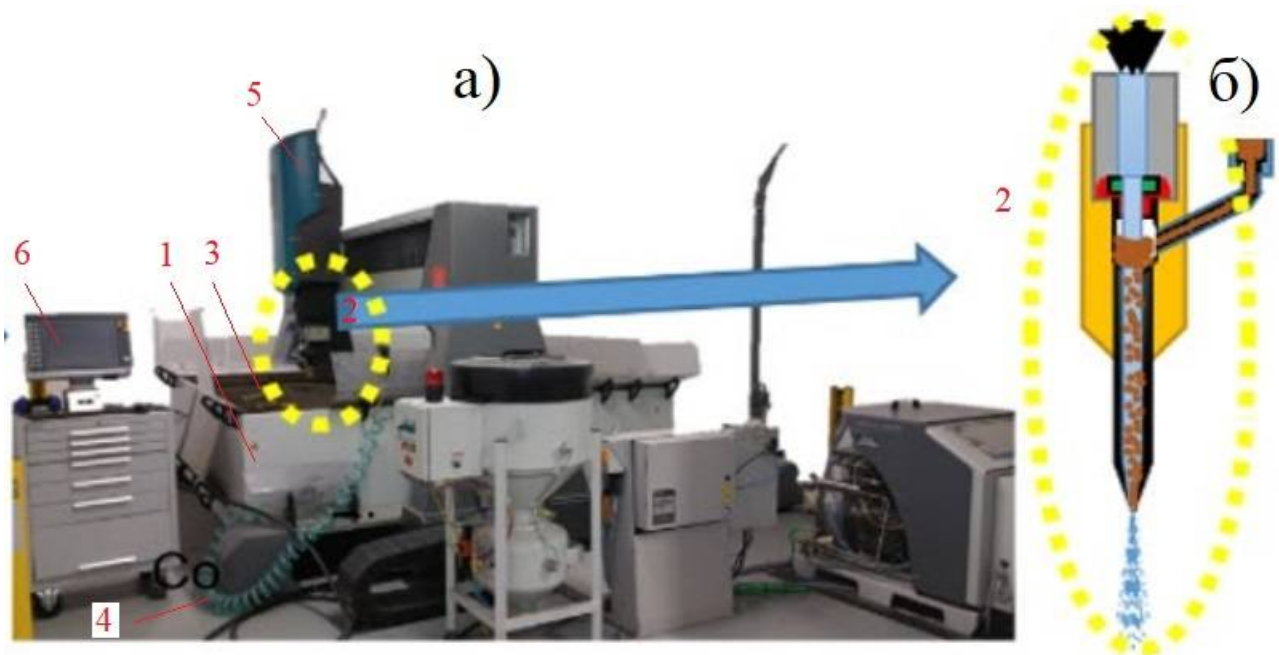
Загальний вигляд ГАО-агрегату (а) та схема ріжучої головки (б)
